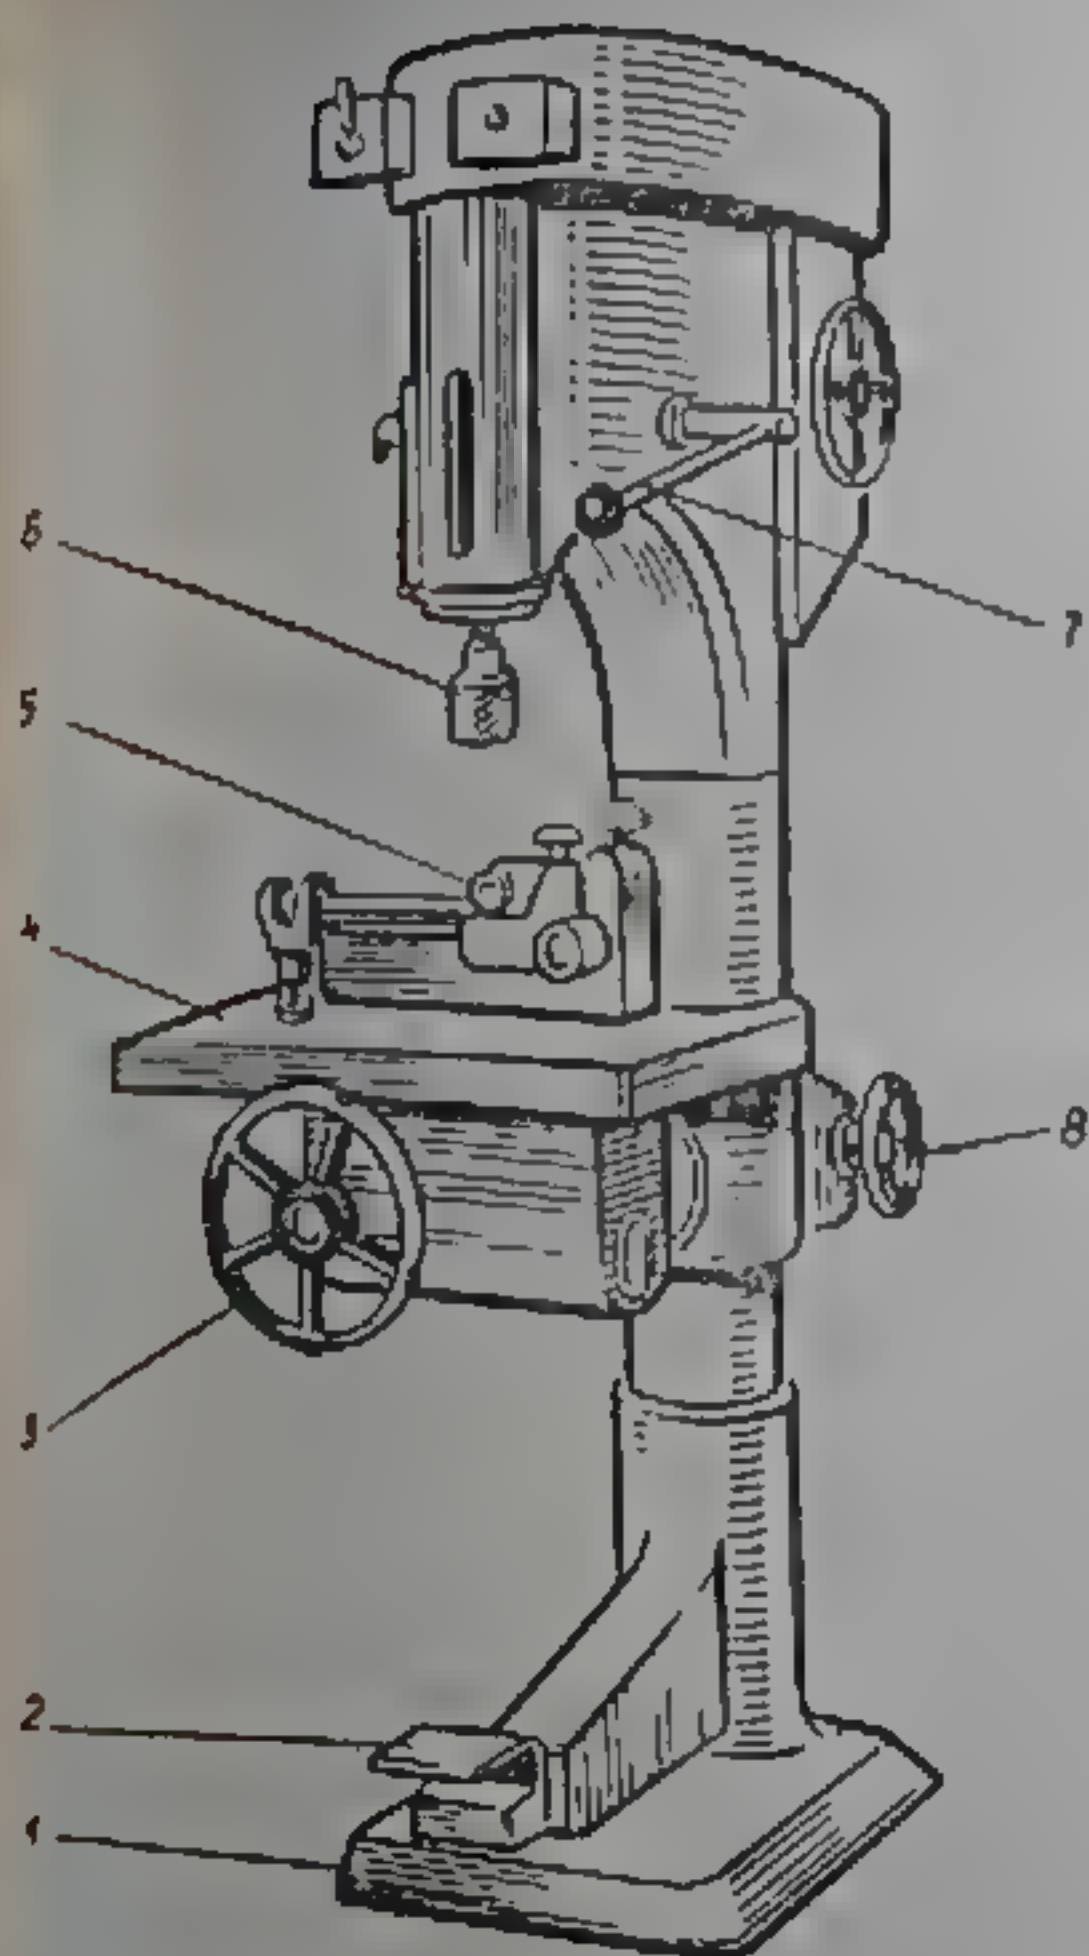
Вертикальный сверлильно-пазовальный станок:
